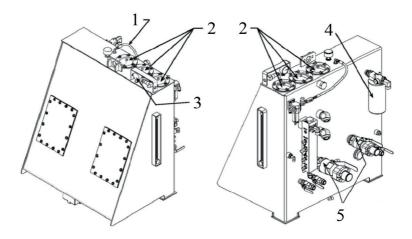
Расположение фильтра для слива: 1 – напорный шланг бака; 2 – модули фильтров бака; 3 – датчик давления бака; 4 – фильтр слива картера; 5 – главные шаровые клапаны гидробака
